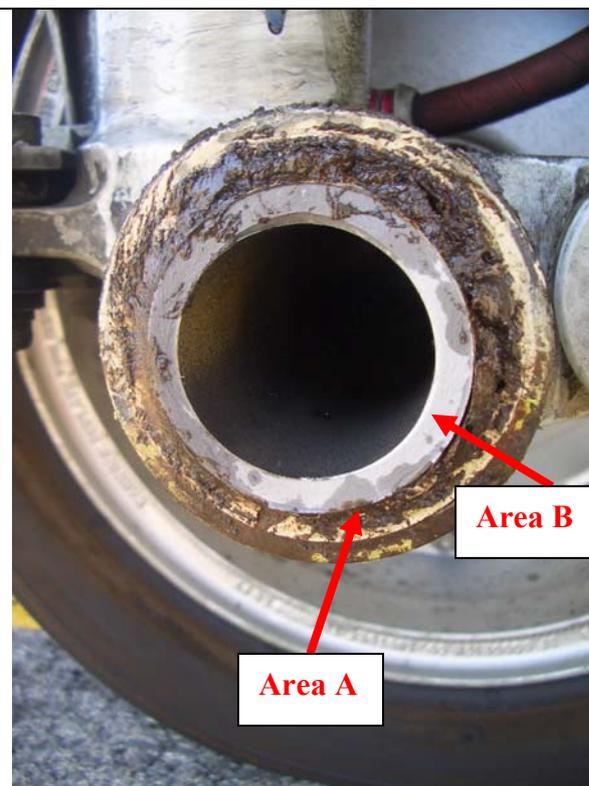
superficie di rottura dell'assale collegata all'inner cylinder, aree A e B.
